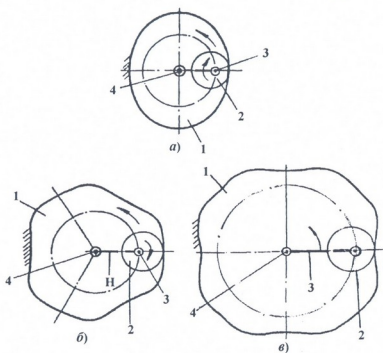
Планетарные передачи с эксцентричными круглыми и некруглыми цилиндрическими колесами
